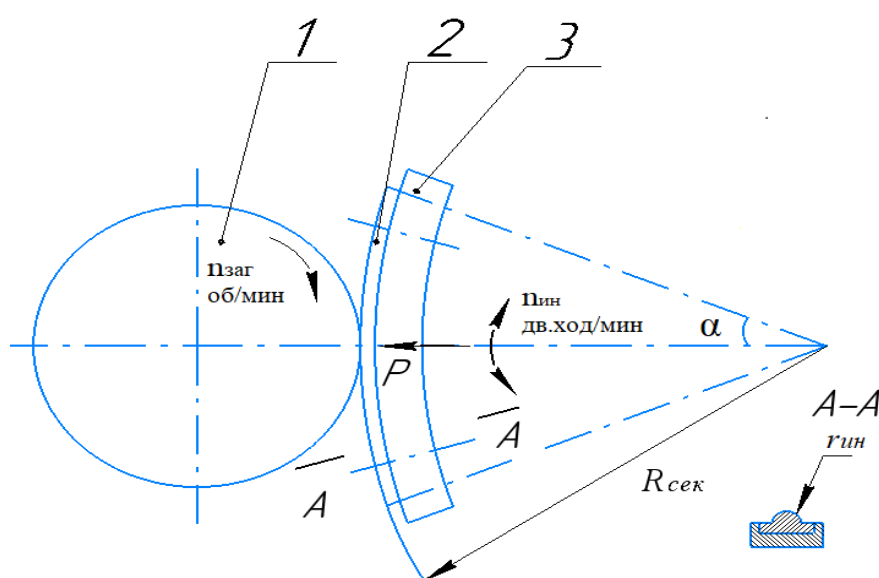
Схема маятникового поверхностного пластического деформирования
